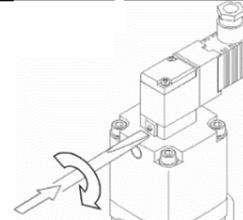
Verriegelbare Handhilfsbetätigung mit Schlitzausführung
